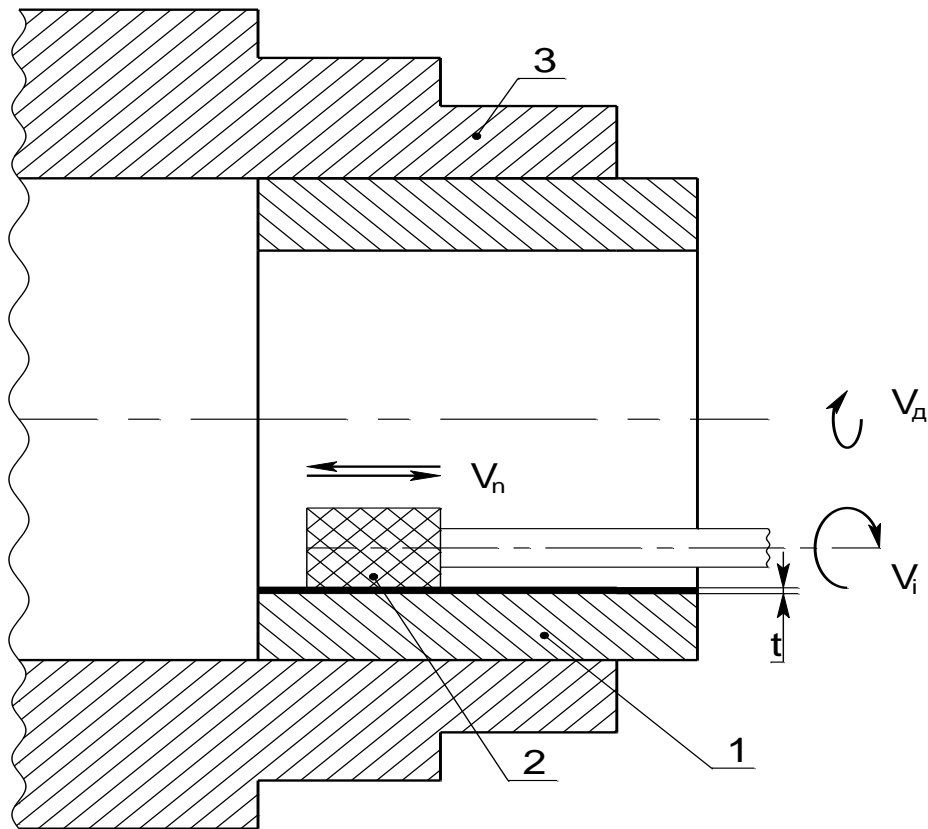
Спосіб тонкої абразивної обробки циліндричних отворів деталей обертання з високолегованих композитів
